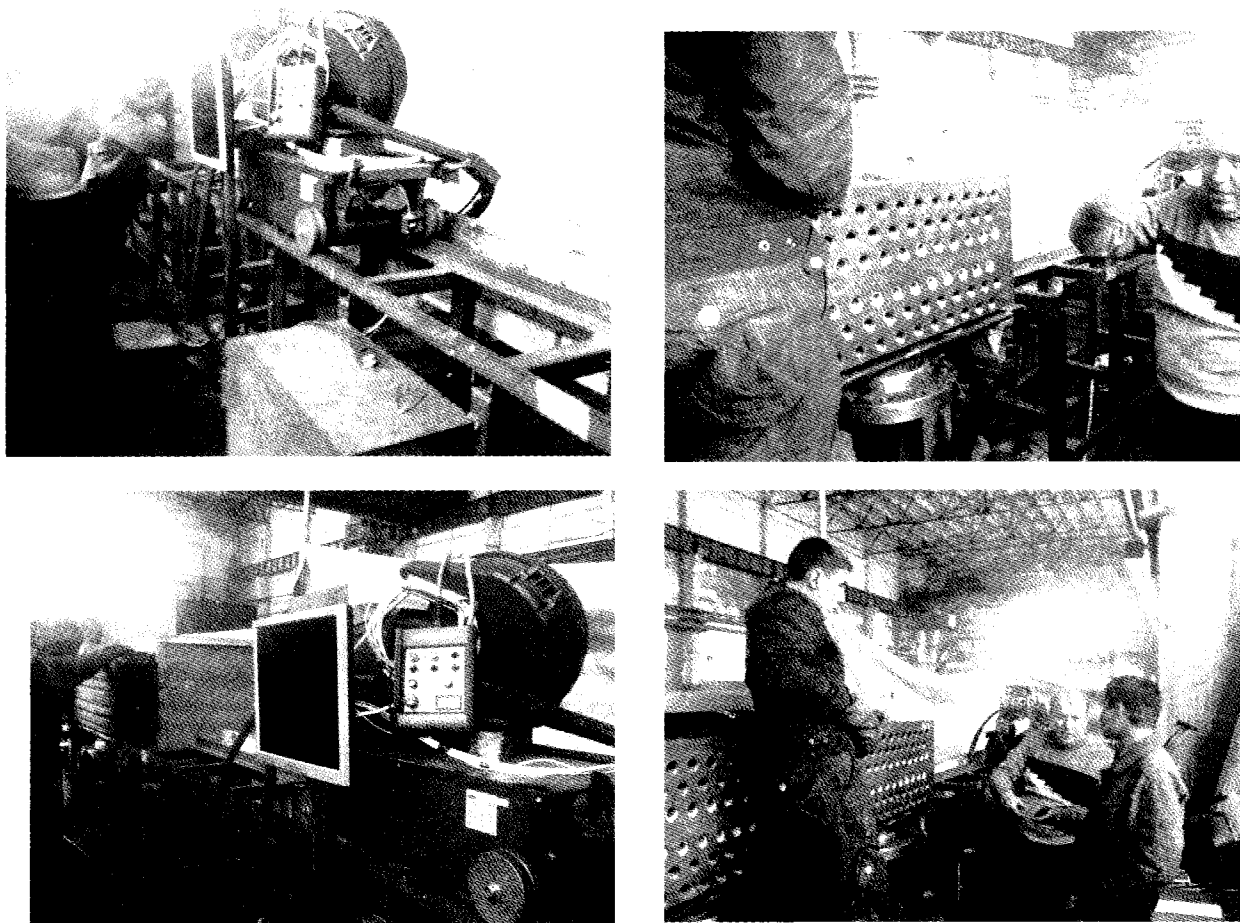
Модель расположения приспособления для автоматической сварки внутри камеры АВО
